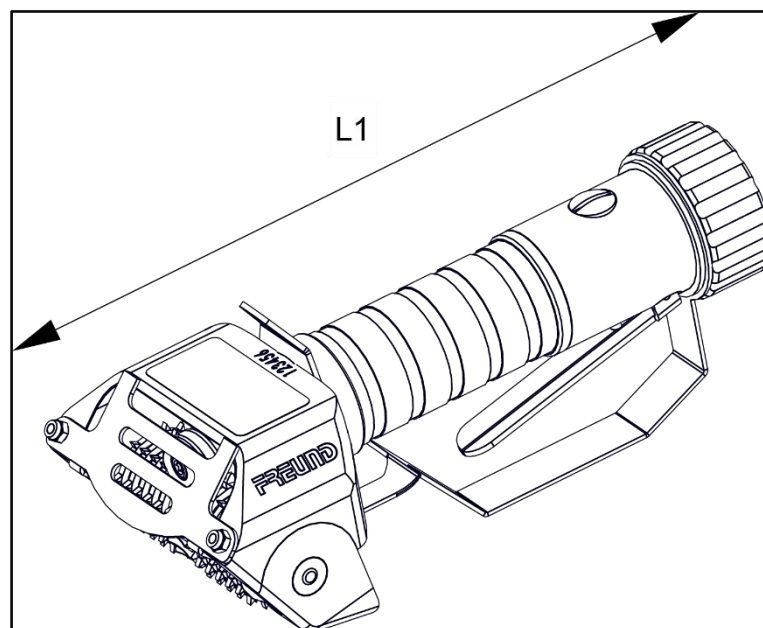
Hand-Skinner HSK8-P5 в сборе
